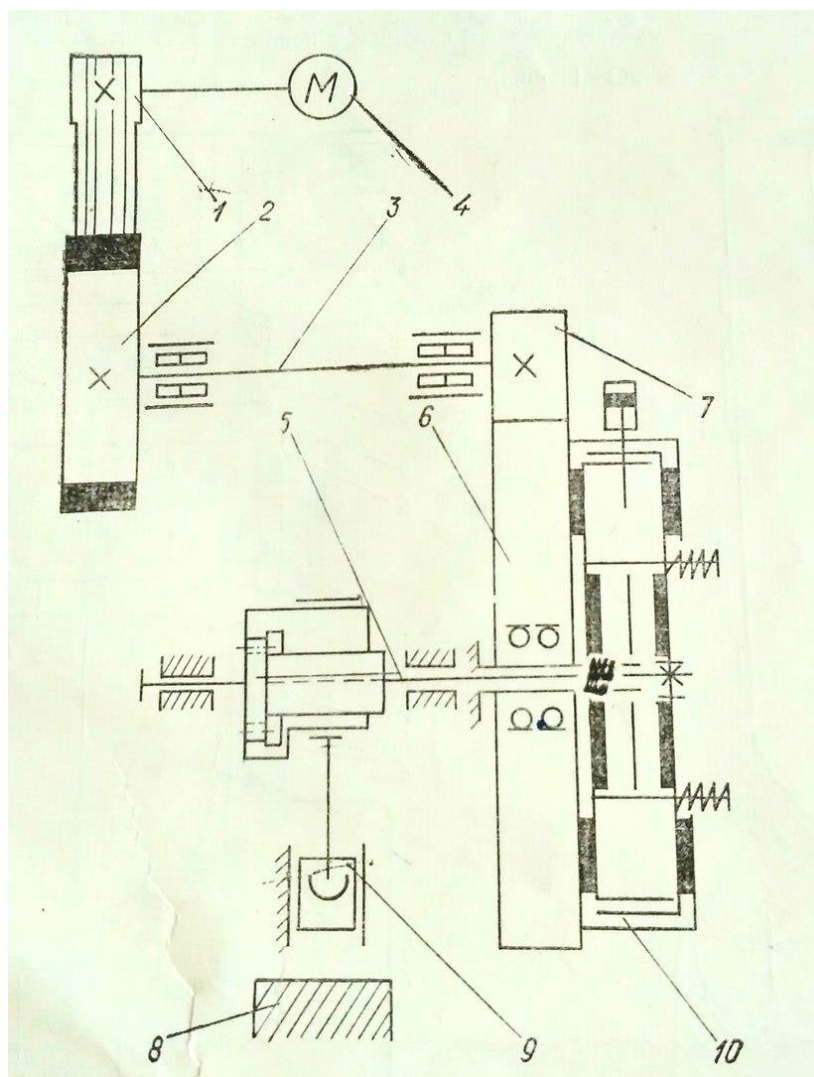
Кинематическая схема прессы модели К-2130Б: 1- шкив; 2 – маховик; 3 – вспомогательный вал; 4 – электродвигатель; 5- вал главный; 6,7 – шестерни; 8 – стол; 9 – ползун; 10- муфта-тормоз.
